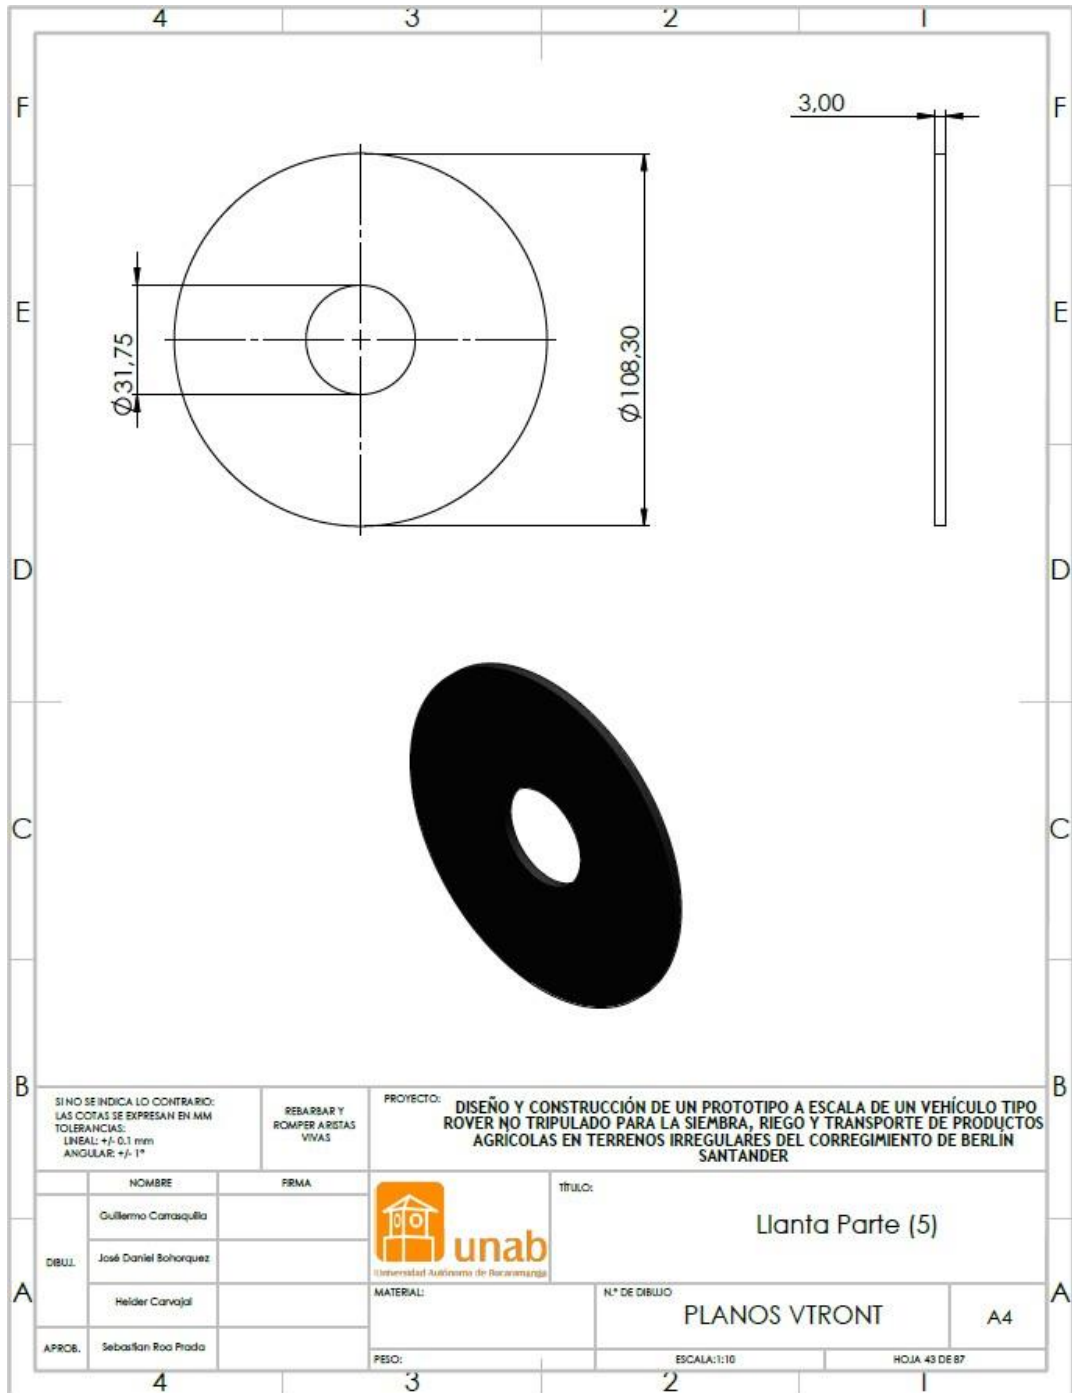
Plano de corte de lámina para la llanta parte 5.
